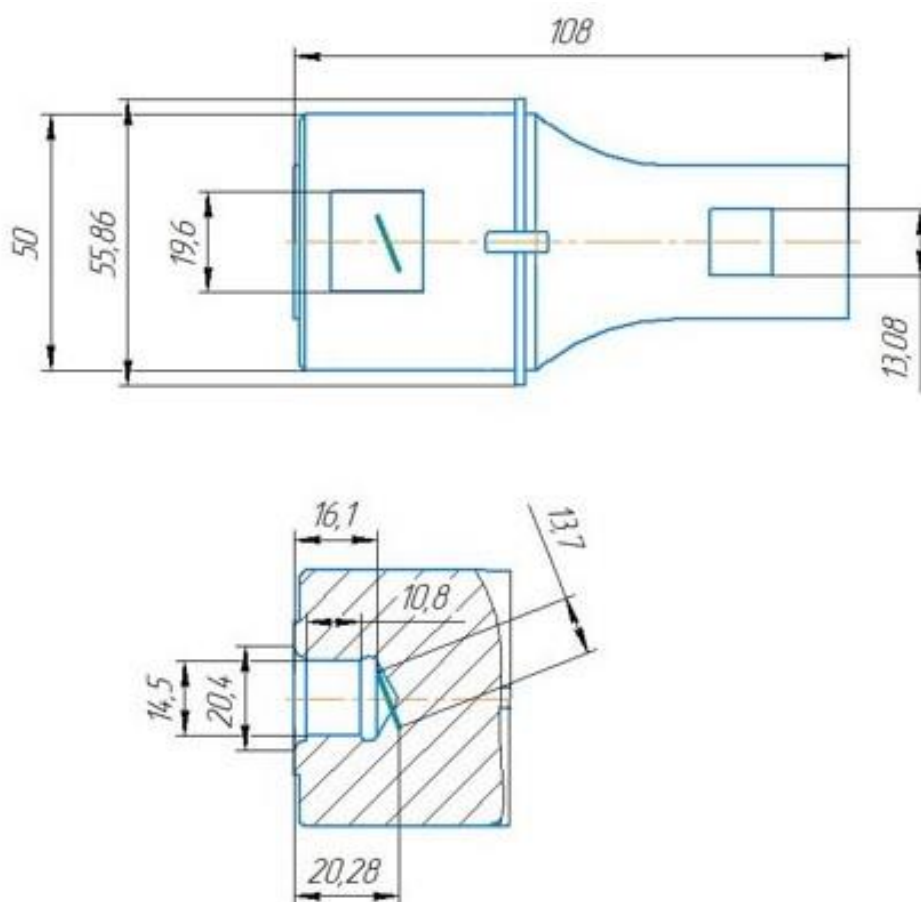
Чертеж образца с указанием резьбового соединения
